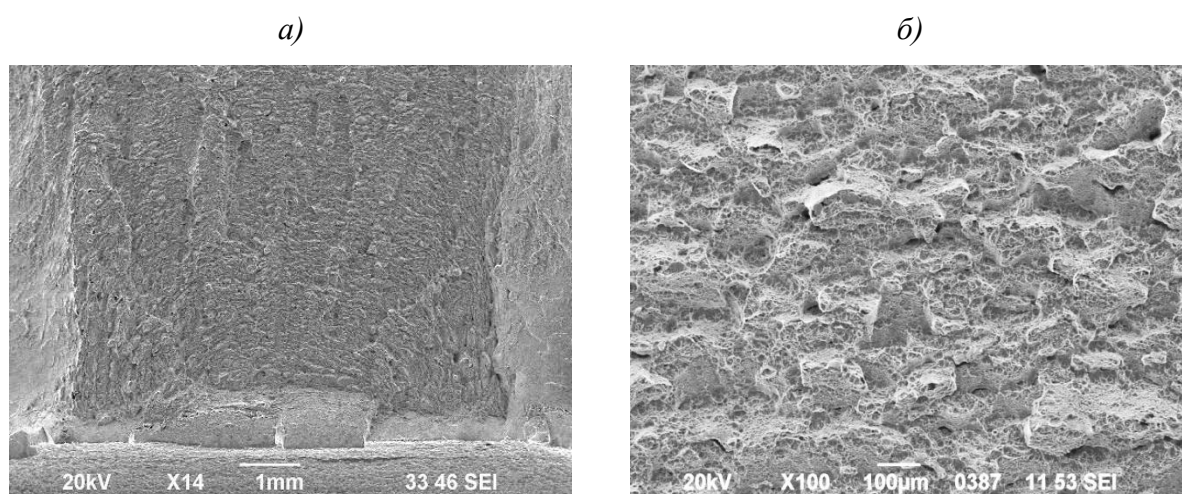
Строение излома образца, вырезанного из прутка стали ВКС-180ИД изготовленной по стандартной технологии
